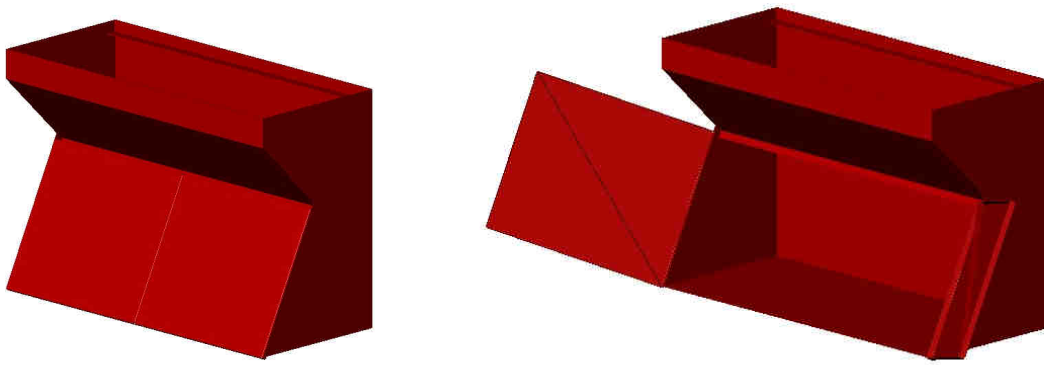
Diseño de la estructura base de la máquina de rotomoldeo.
